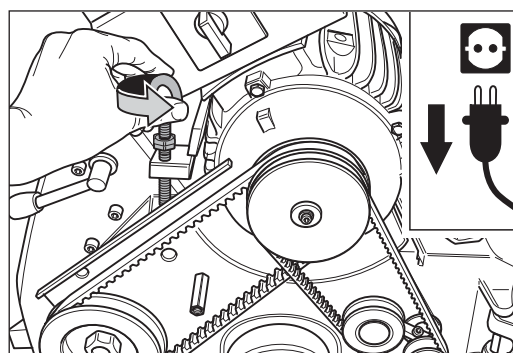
Die Ringschraube am Motor gegen den Uhrzeigersinn drehen.
